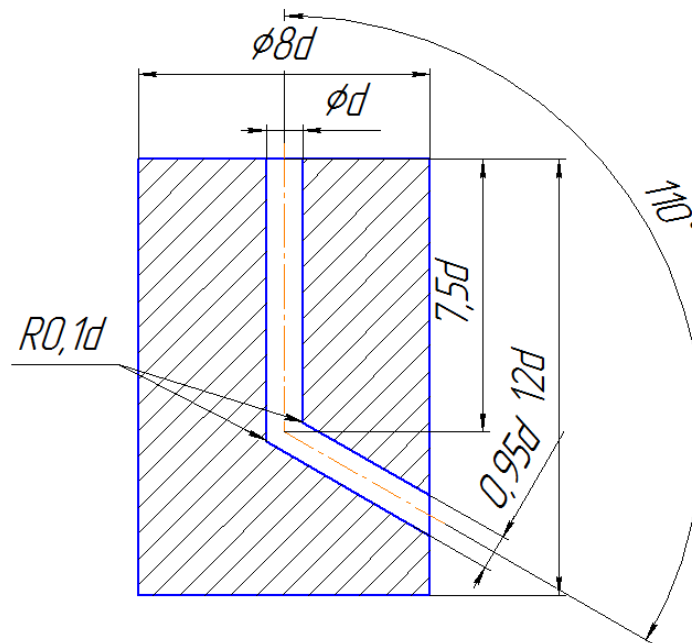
Схема матрицы для РКУП цилиндрической заготовки
